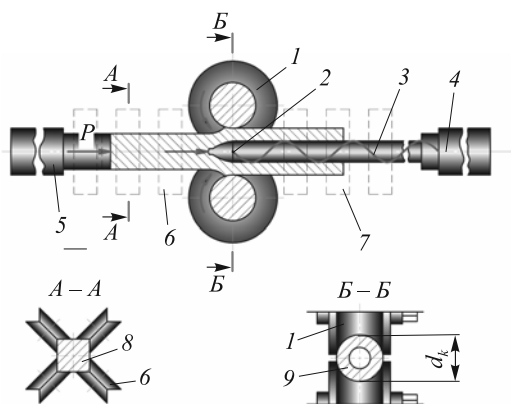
Схема процесса пресс-валковой прошивки трубной заготовки:
